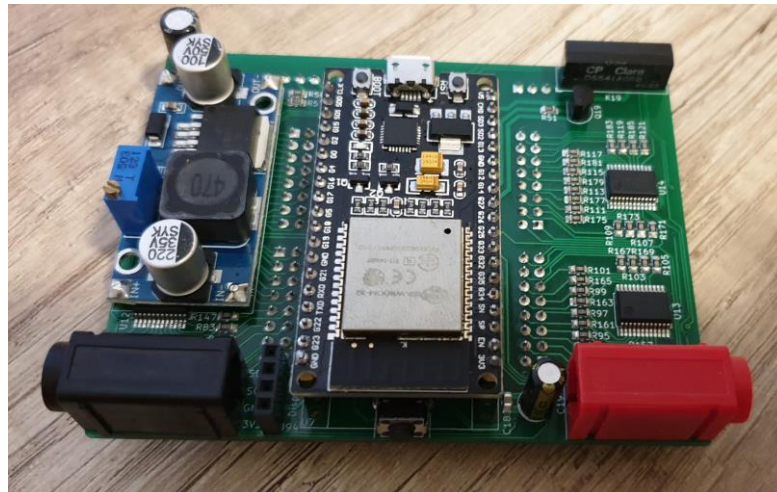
Zasazení Elnec přípravku pro úplné manuální ověření parametrů do sestavy
